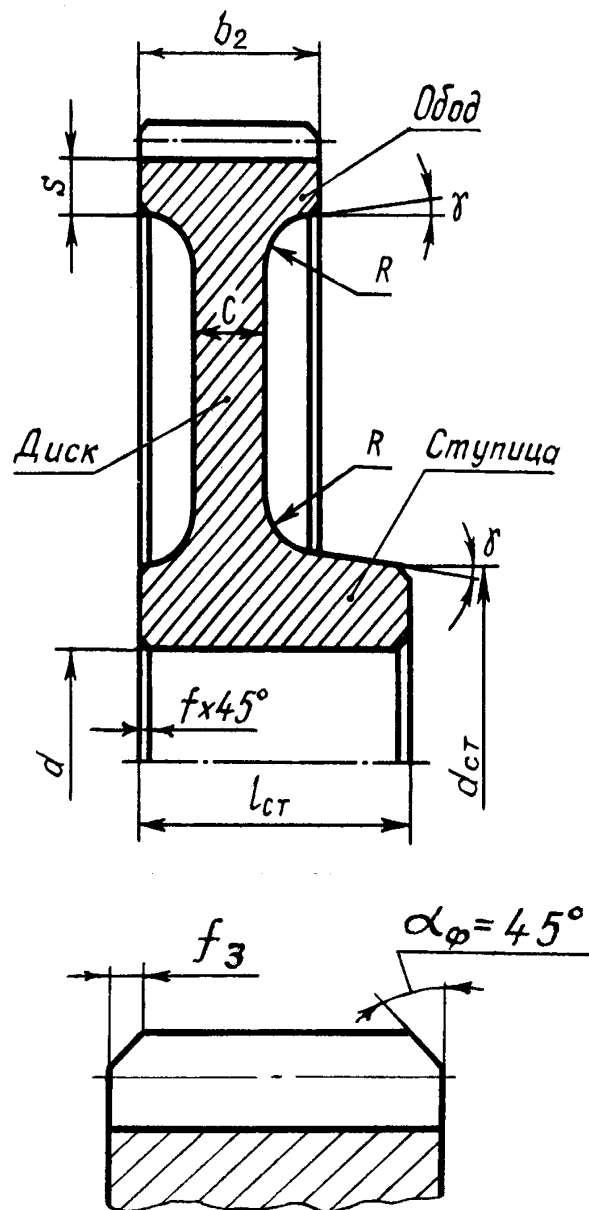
Размеры конструктивных элементов насадных цилиндрических косозубых колес редуктора
